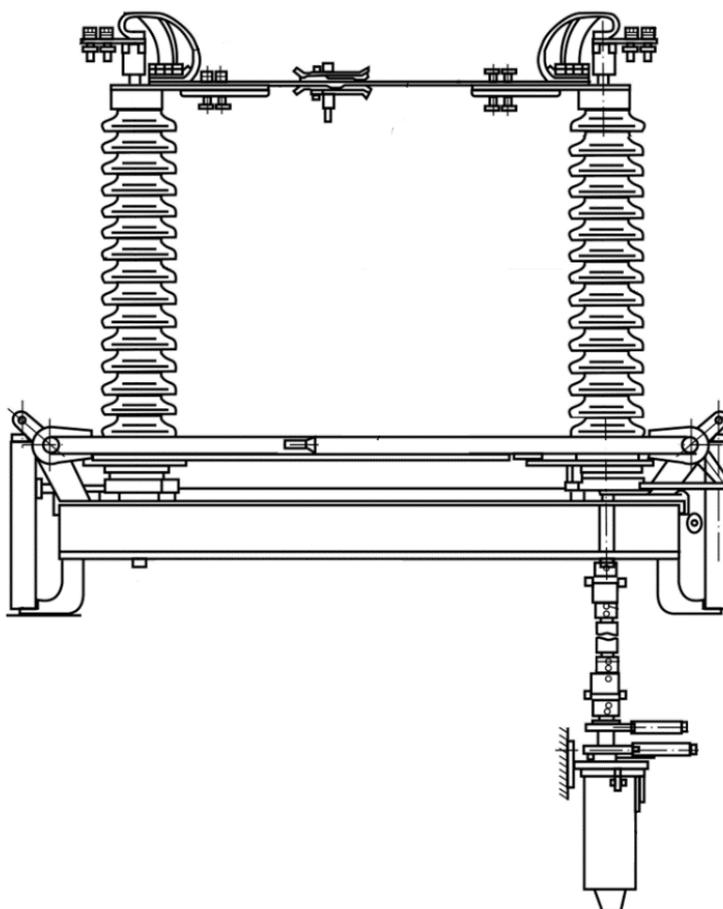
Внешний вид разъединителя марки РНДЗ-16-110/1000
